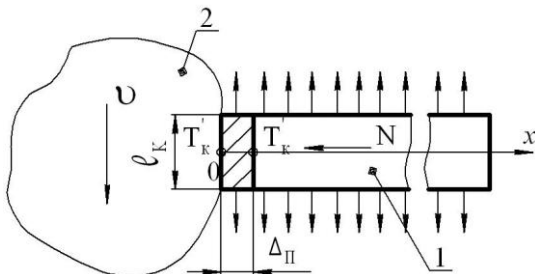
Модель пары трения с покрытием на инструментальном материале: 1 - стержень с покрытием; 2 - заготовка
